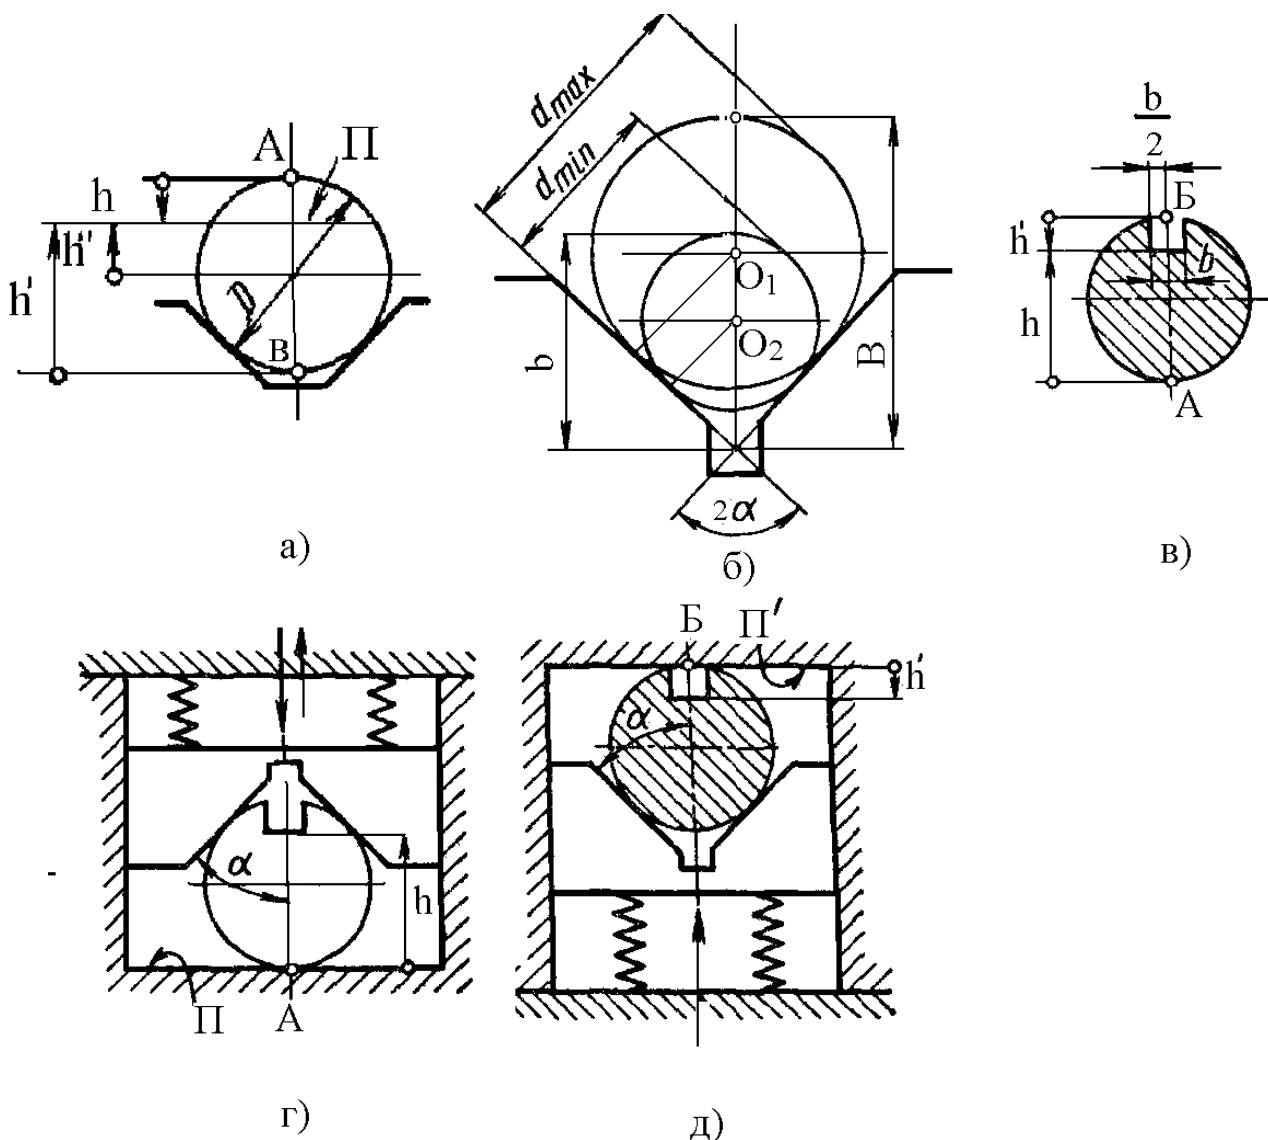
Схемы для определения погрешности установки деталей по наружной цилиндрической поверхности
